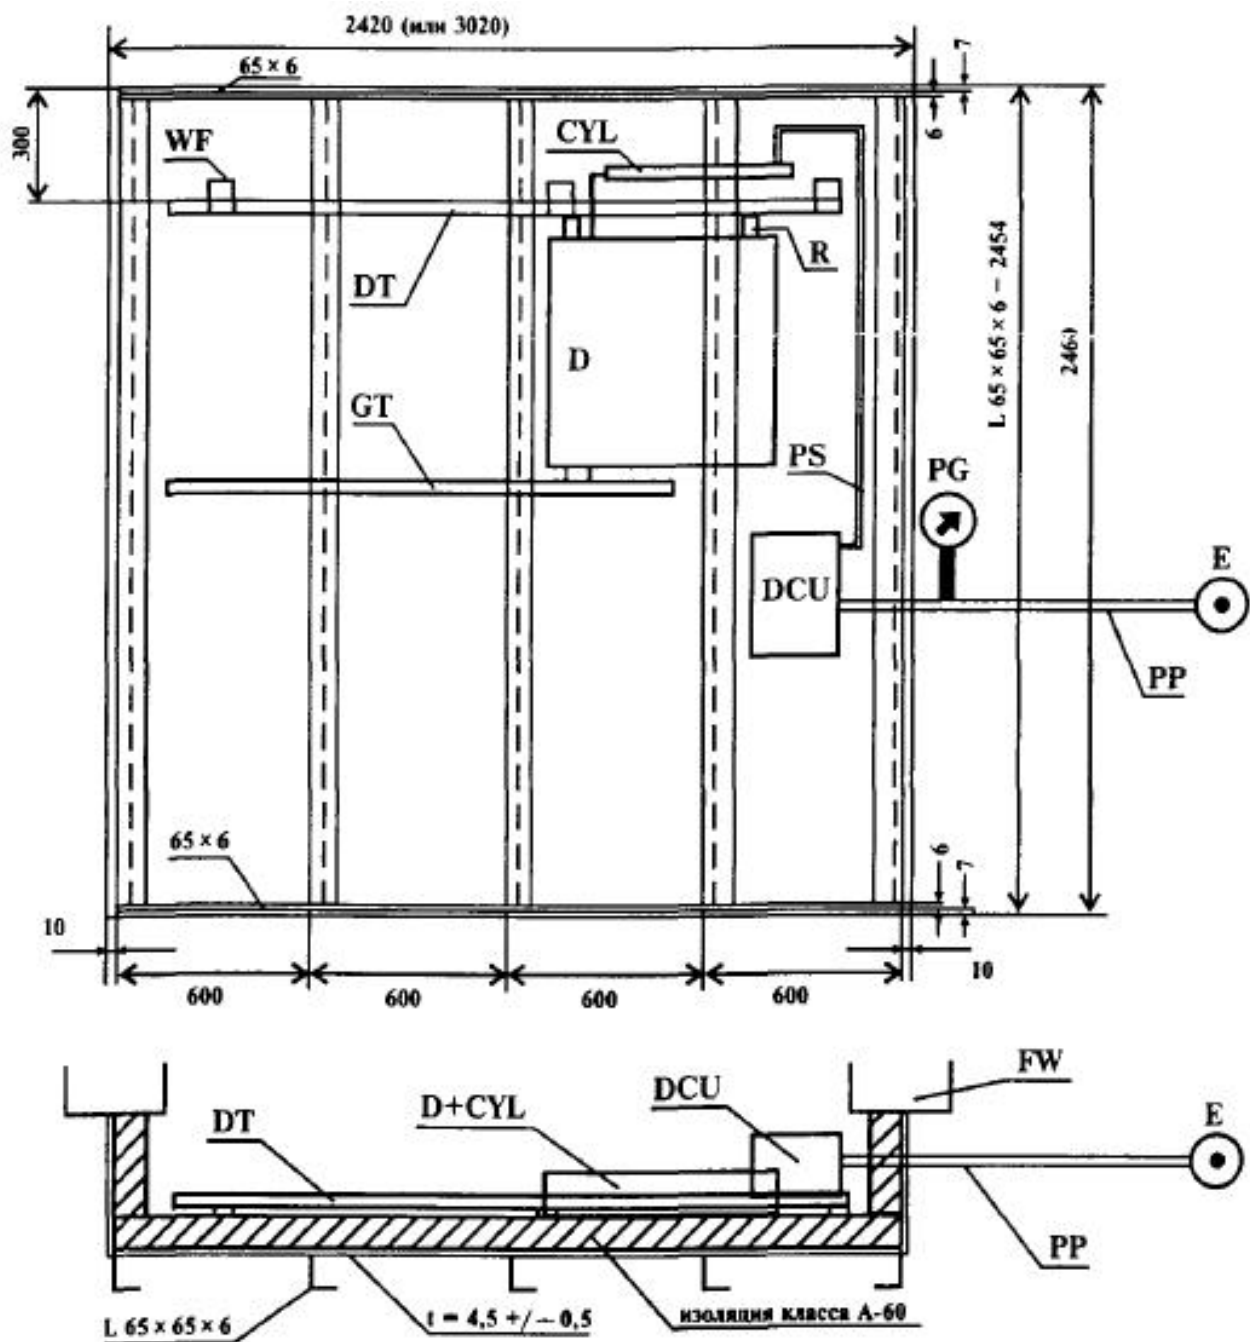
Основа конструкции для установки прототипа системы управления противопожарными дверьми
